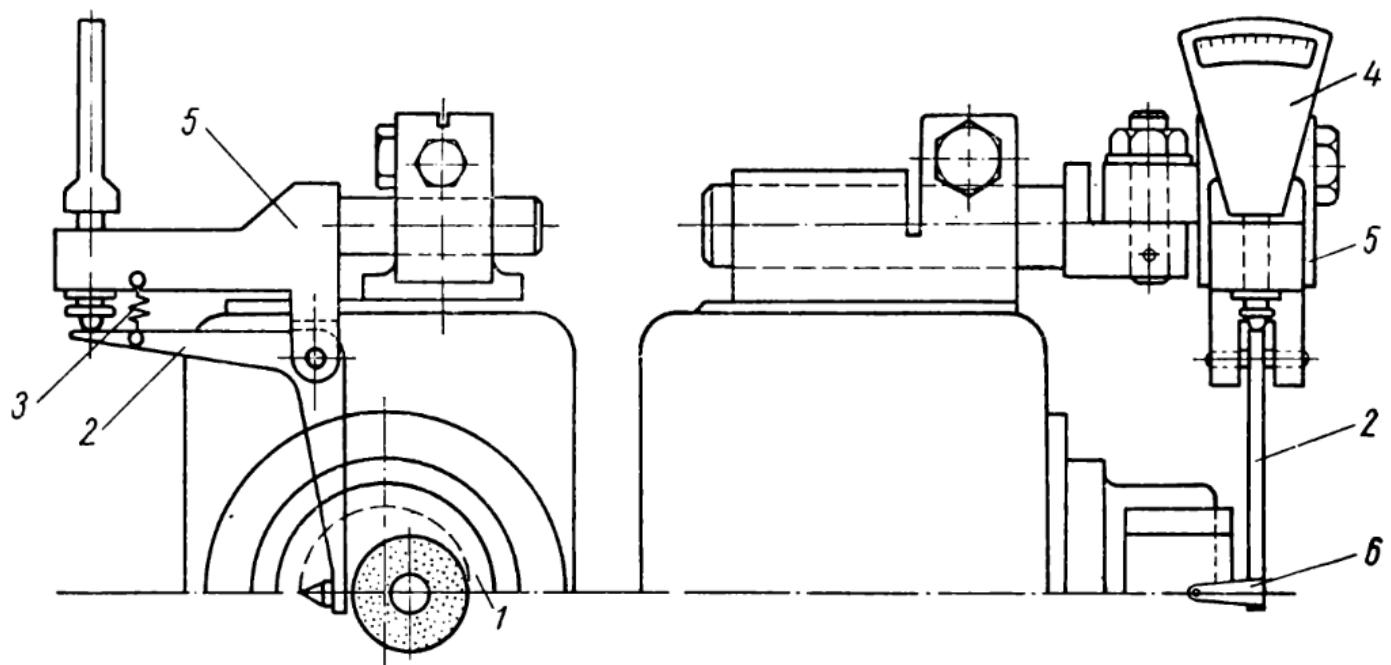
Рычажное одноконтактное приспособление для измерения отверстия в процессе шлифования
